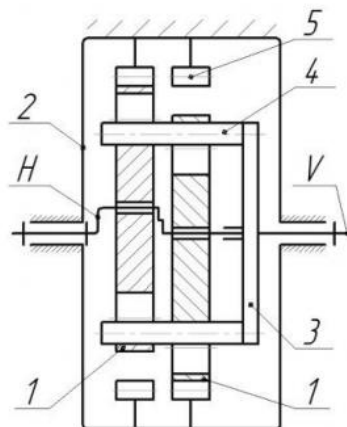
Кінематична схема редуктора типу К-Н-V з двома сателітами
